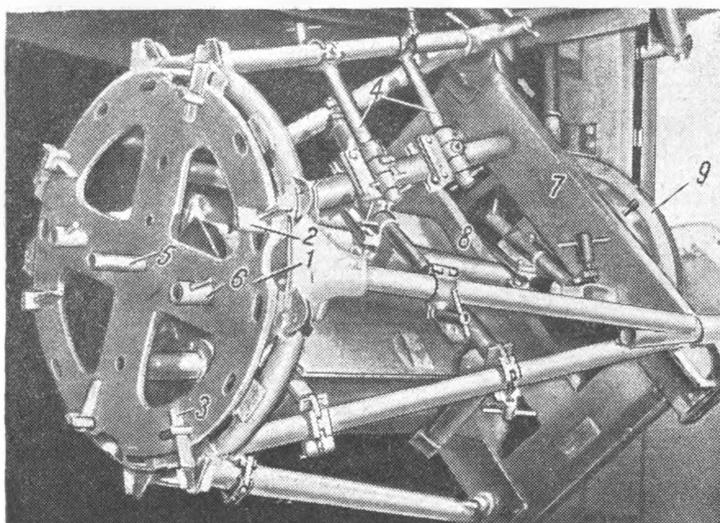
Приспособление для сборки и прихватки кольца моторамы.
